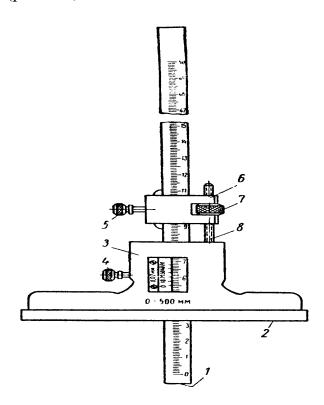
Штангенглубиномер: 1 и 2 — измерительные плоскости; 3 — рамка с нониусом; 4, 5 — стопорный винт; 6 — хомутик; 7 — гайка; 8 — винт
